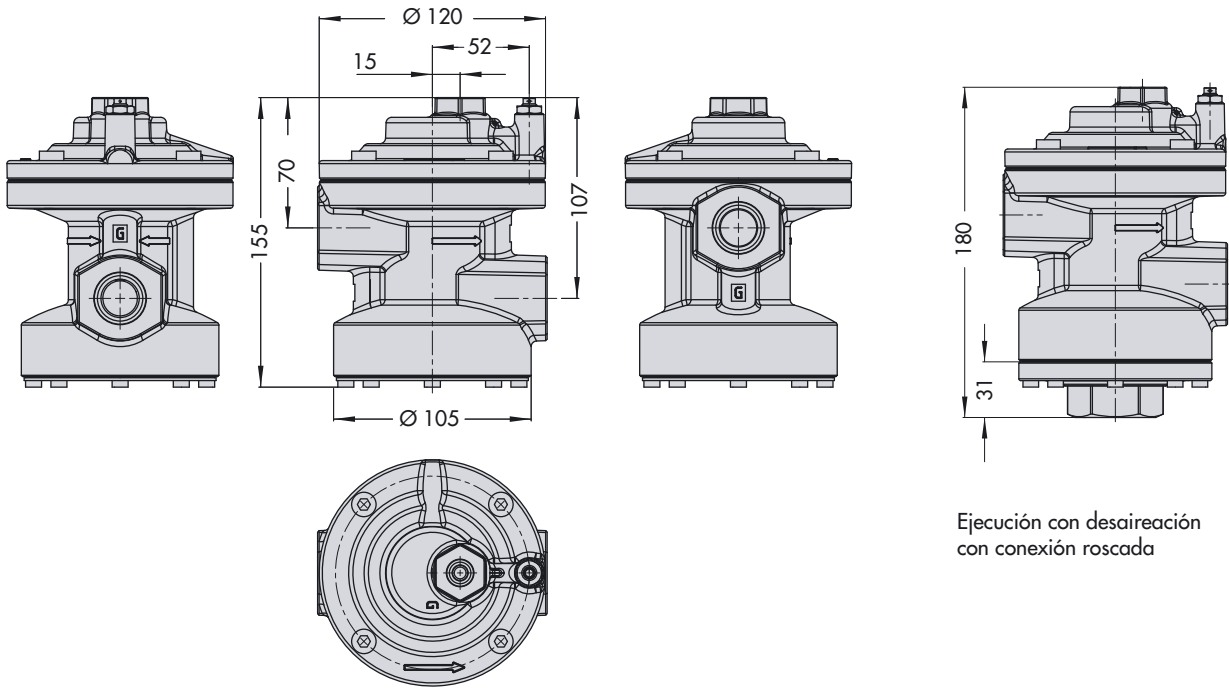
· Dibujo dimensional del Tipo 3755 · Dimensiones en mm
